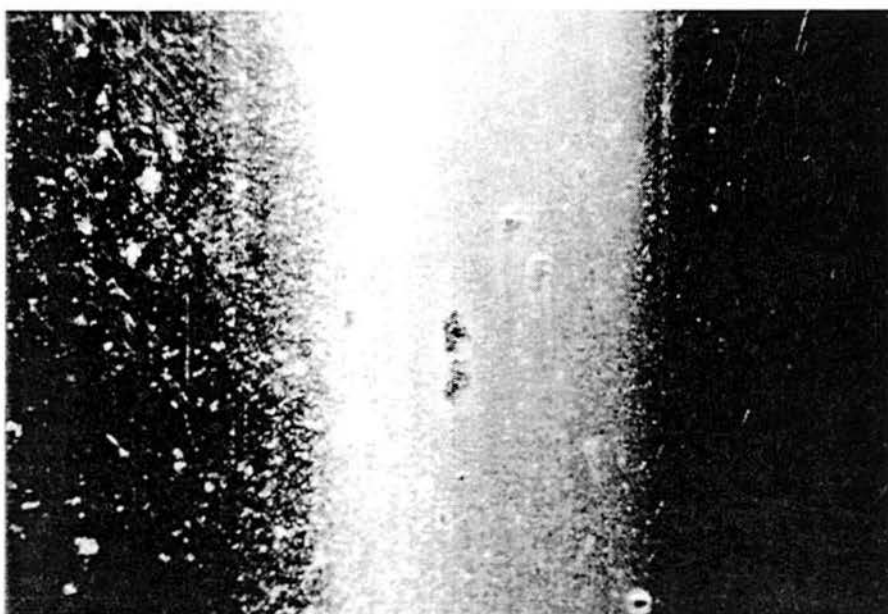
48MVT01D - pista externa LOA, outro detalhe.
